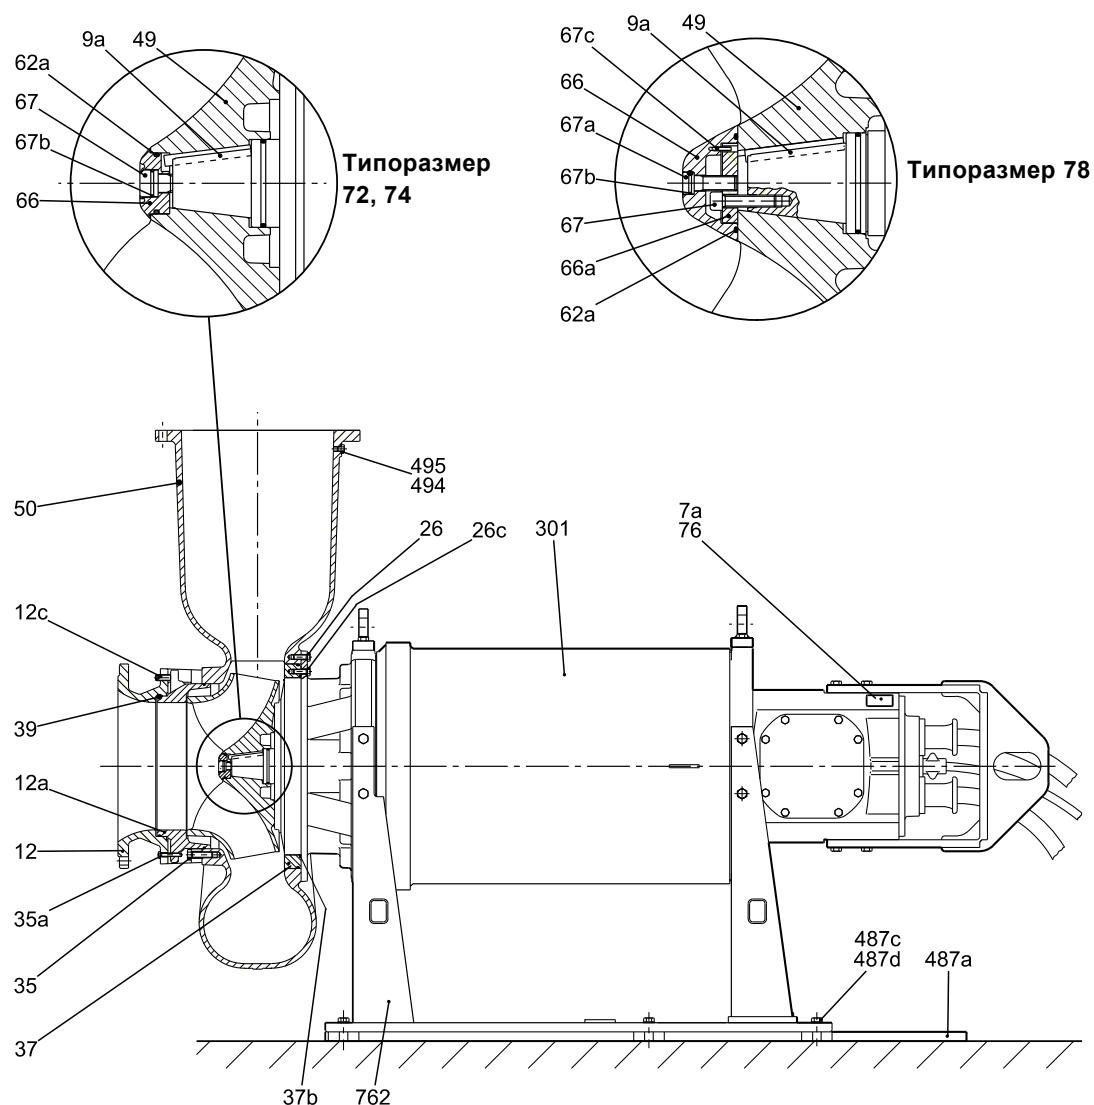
Типоразмеры 72, 74 и 78, сухая установка в горизонтальном положении
